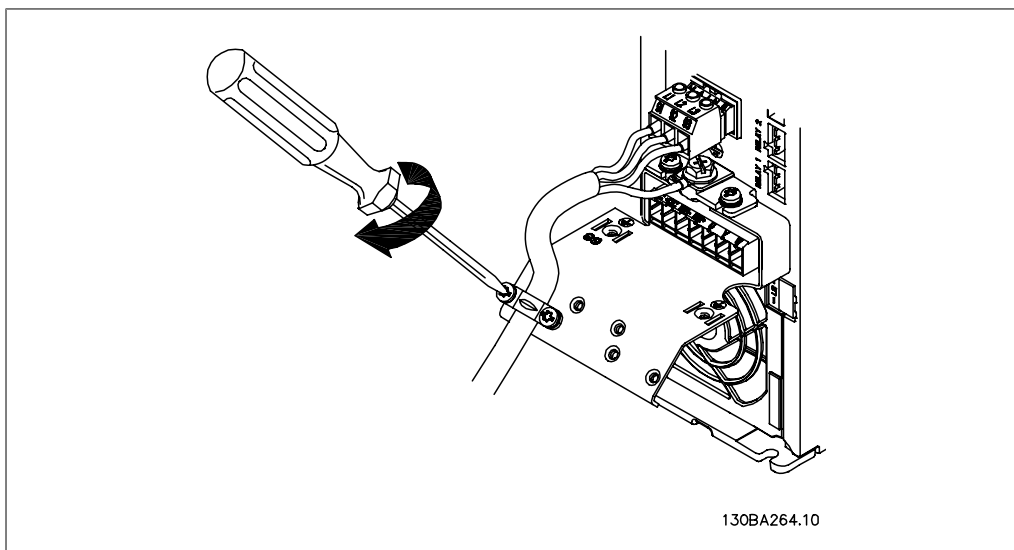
Por último, apriete la abrazadera de montaje de los cables de alimentación.
